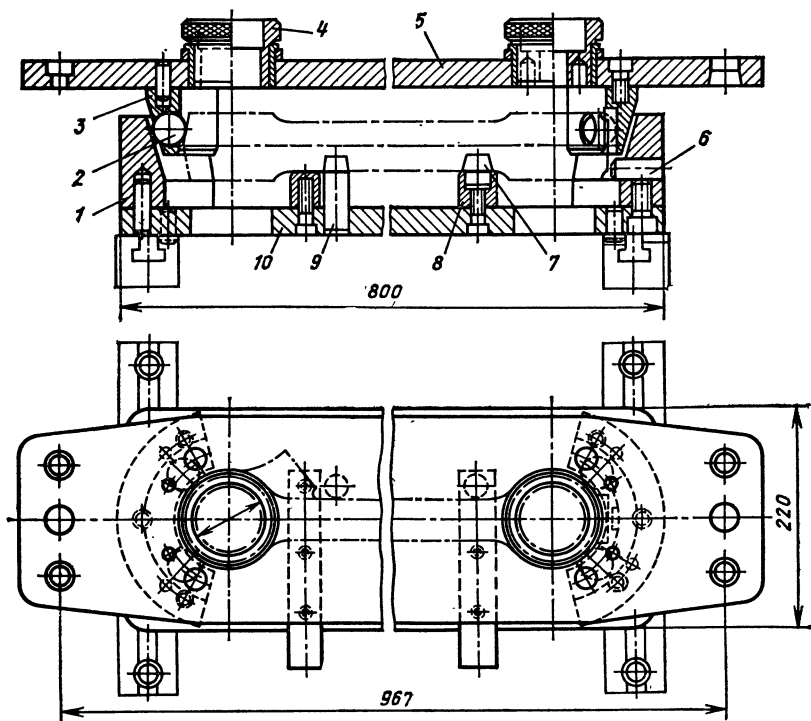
Наладка к порталному скальчатому кондуктору с раздвижными стойками для обработки двух отверстий в головках шатуна
